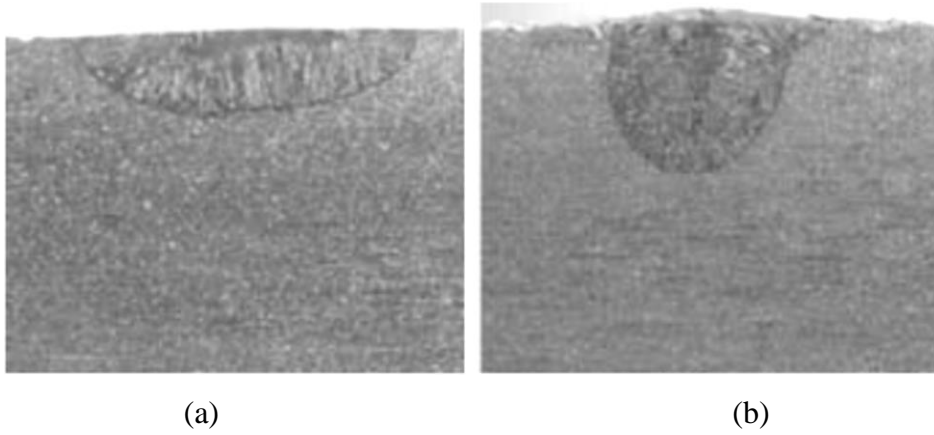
Sessões da soldagem (a) EBW e (b) A-EBW com as mesmas condições de soldagem.
